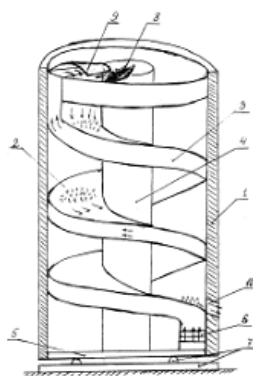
Печь для прокалки сыпучих материалов: 1 – корпус, 2 – полая винтовая поверхность, 3 – образующей жаровой канал, 4 – осевая труба, 5 – основание, 6 – горелка, 7 – вибраторы с виброопорами, 8 – загрузочное приспособление, 9 – козырек, 10 – разгрузочное окно
